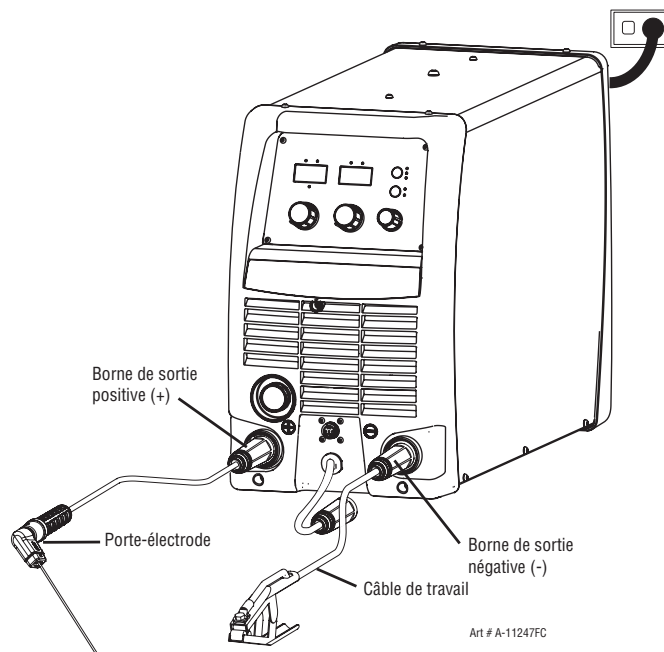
Configuration pour soudage manuel à l'arc.
